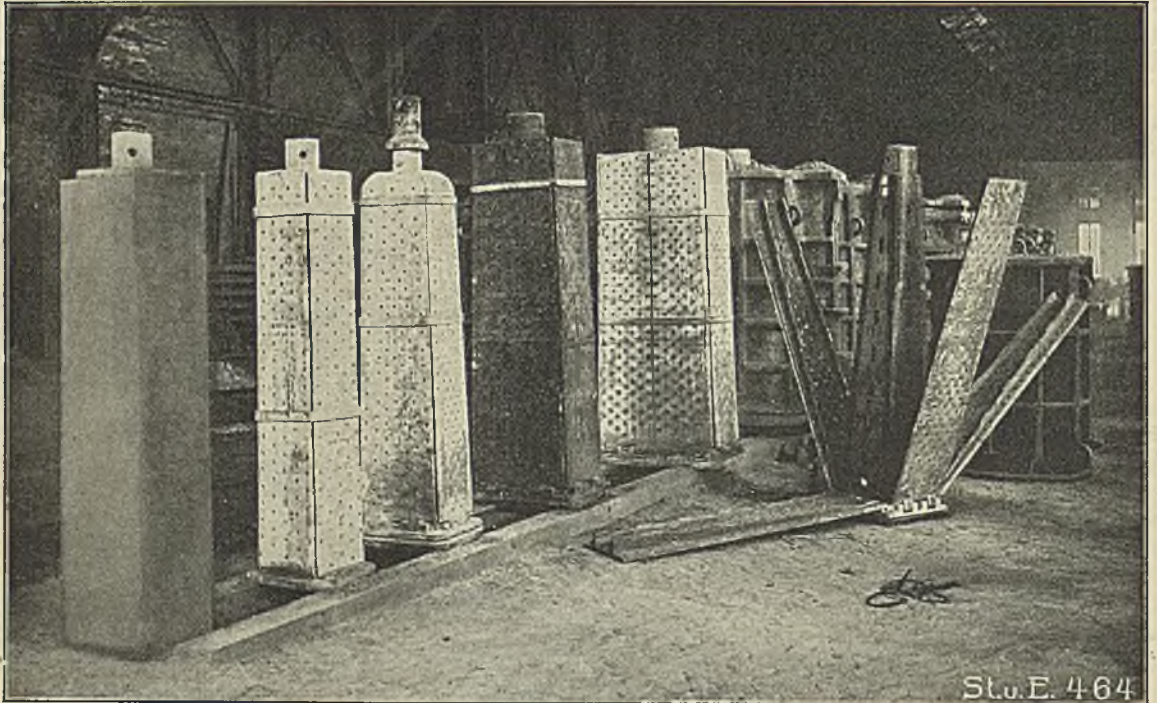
Kernspindeln und fertiger Kern für Kokillen.
